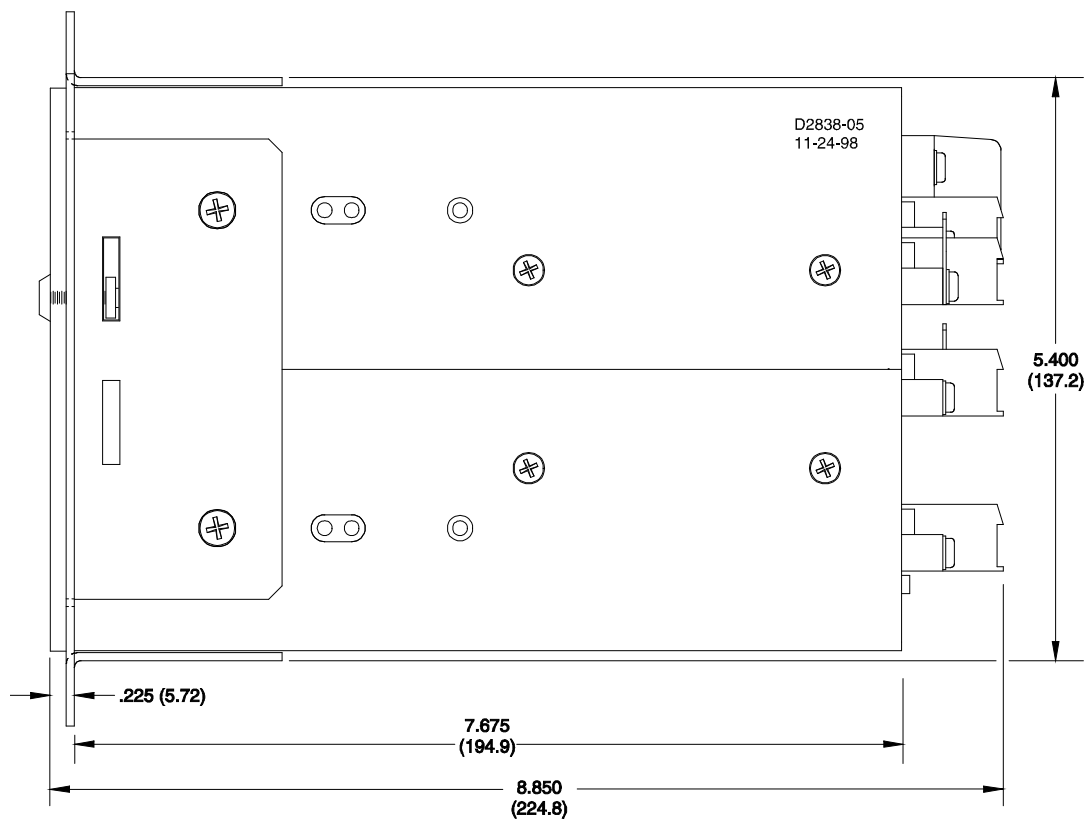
Dimensions du stabilisateur PSS-100 pour un montage sur panneau, Vue de côté
